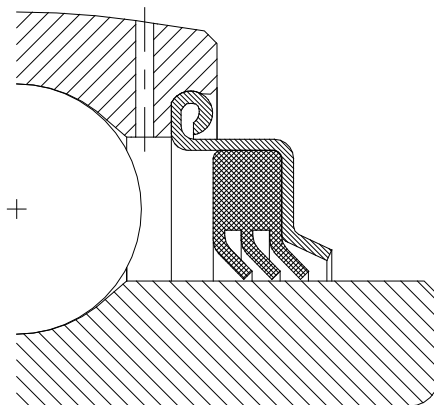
уплотнение типа P3 корпусных подшипников NKE
